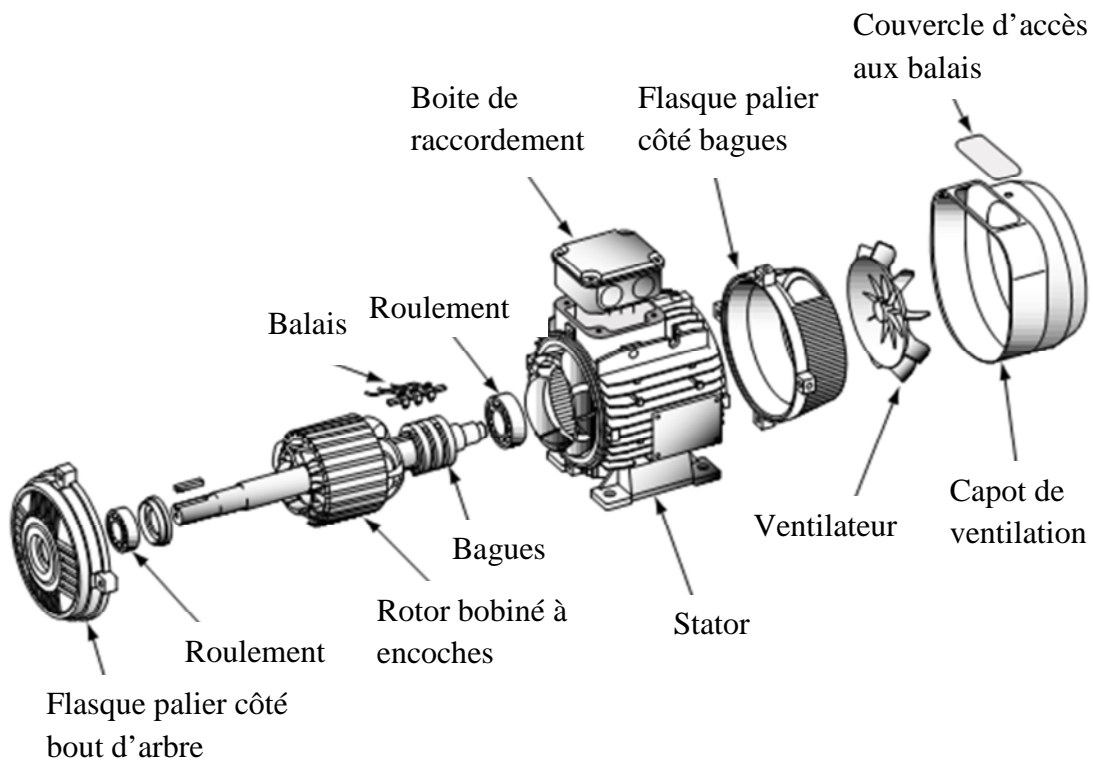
Vue éclaté d'un moteur asynchrone a rotor bobiné.
